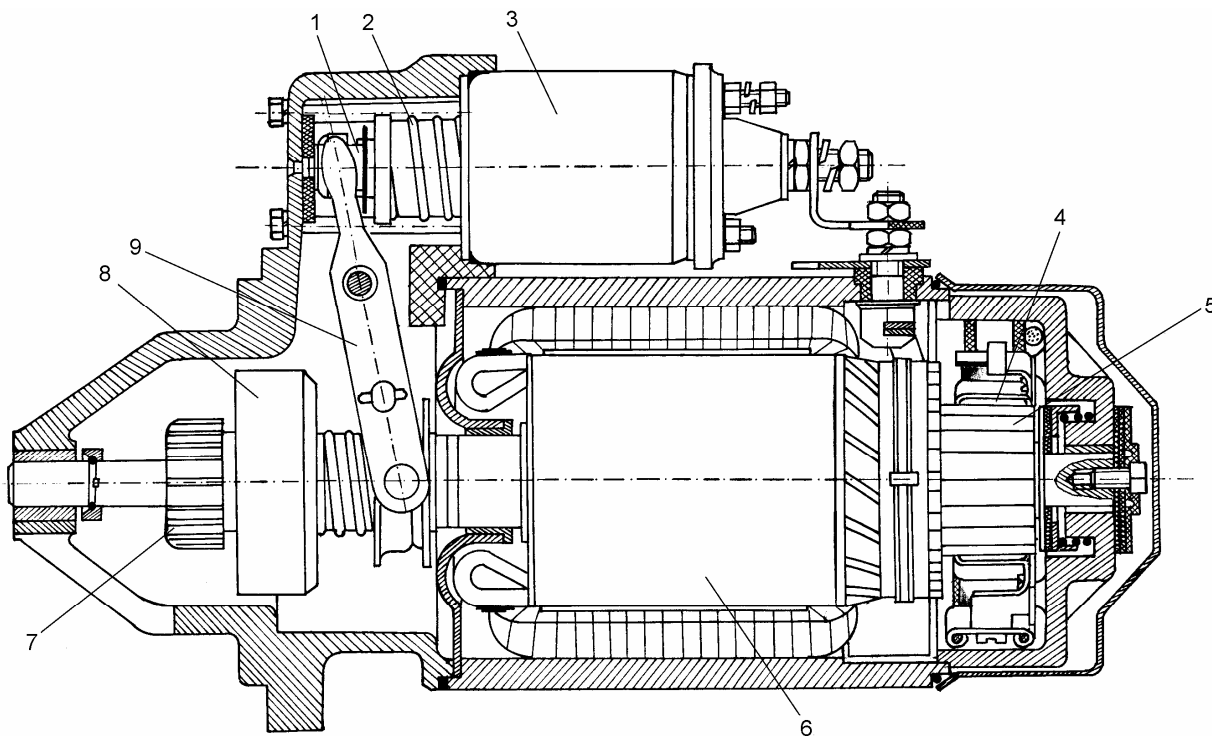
Schema constructivă a demarorului: 1- armătură mobilă; 2- arc revenire; 3- solenoid; 4- perii colectoare; 5- rotor colector; 6- stator; 7- pinion cuplare; 8- cuplaj unisens; 9- levier cuplare
